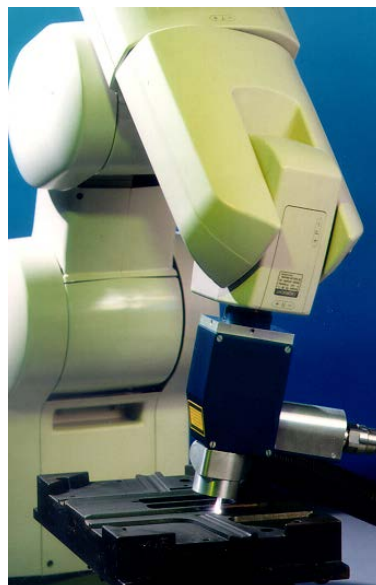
Роботизированные комплексы для лазерной очистки поверхности
